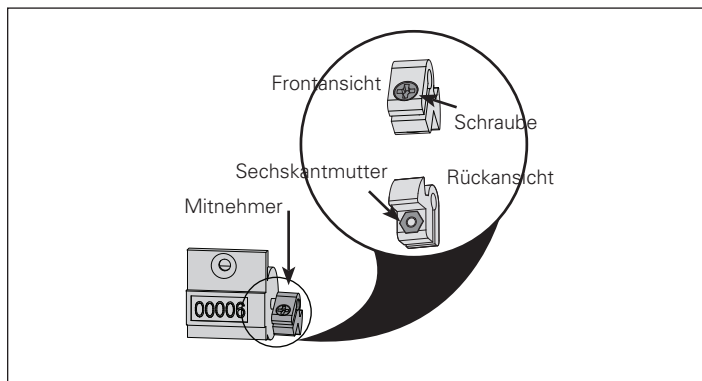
Mit Schraube und Mutter befestigter Mitnehmer
